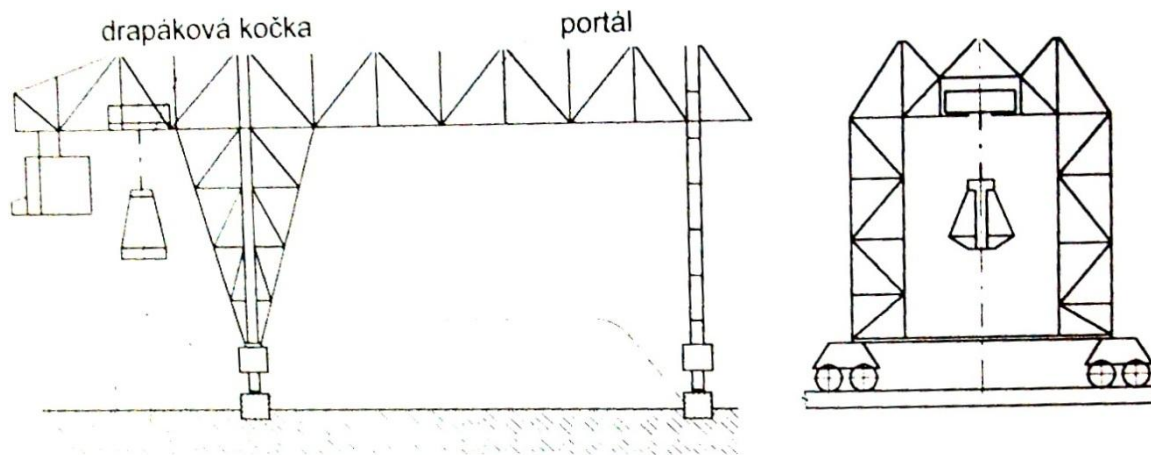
příklad speciálního stohovacího jeřábu [8]
